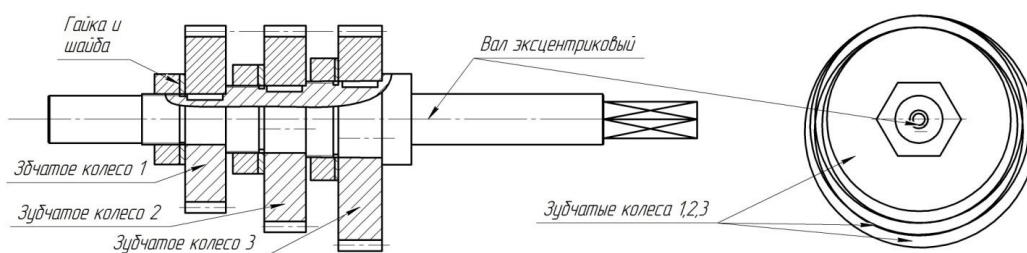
Эскиз блок-вала колес в исполнении сборочной единицы
